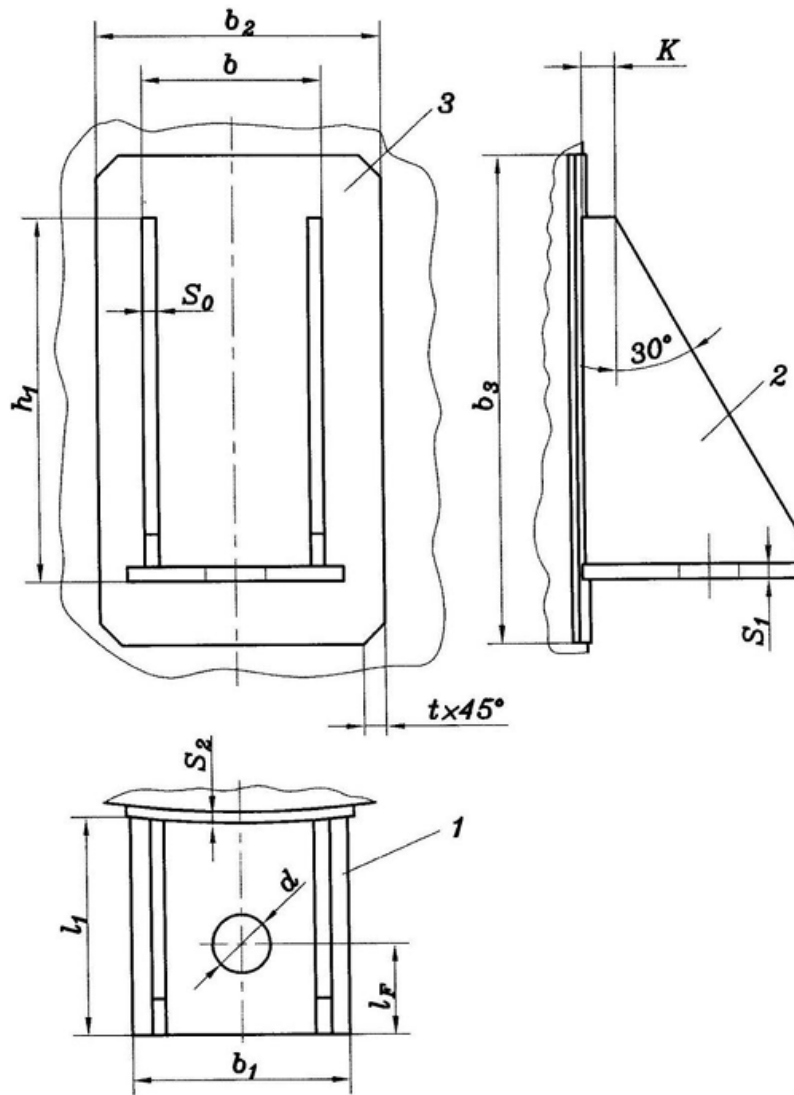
Зварна опорна лапа: 1 – пластина; 2 – ребро; 3 – накладний лист [9]
